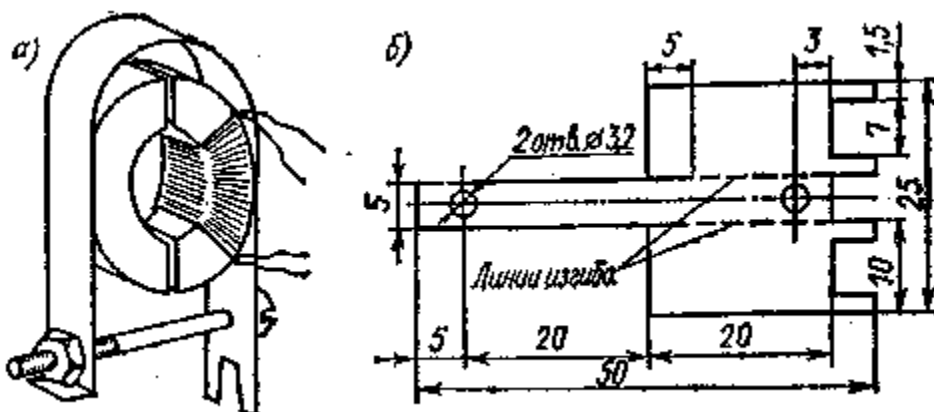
Катушка с регулируемой индуктивностью. а — общий вид; б — развертка корпуса-экрана
